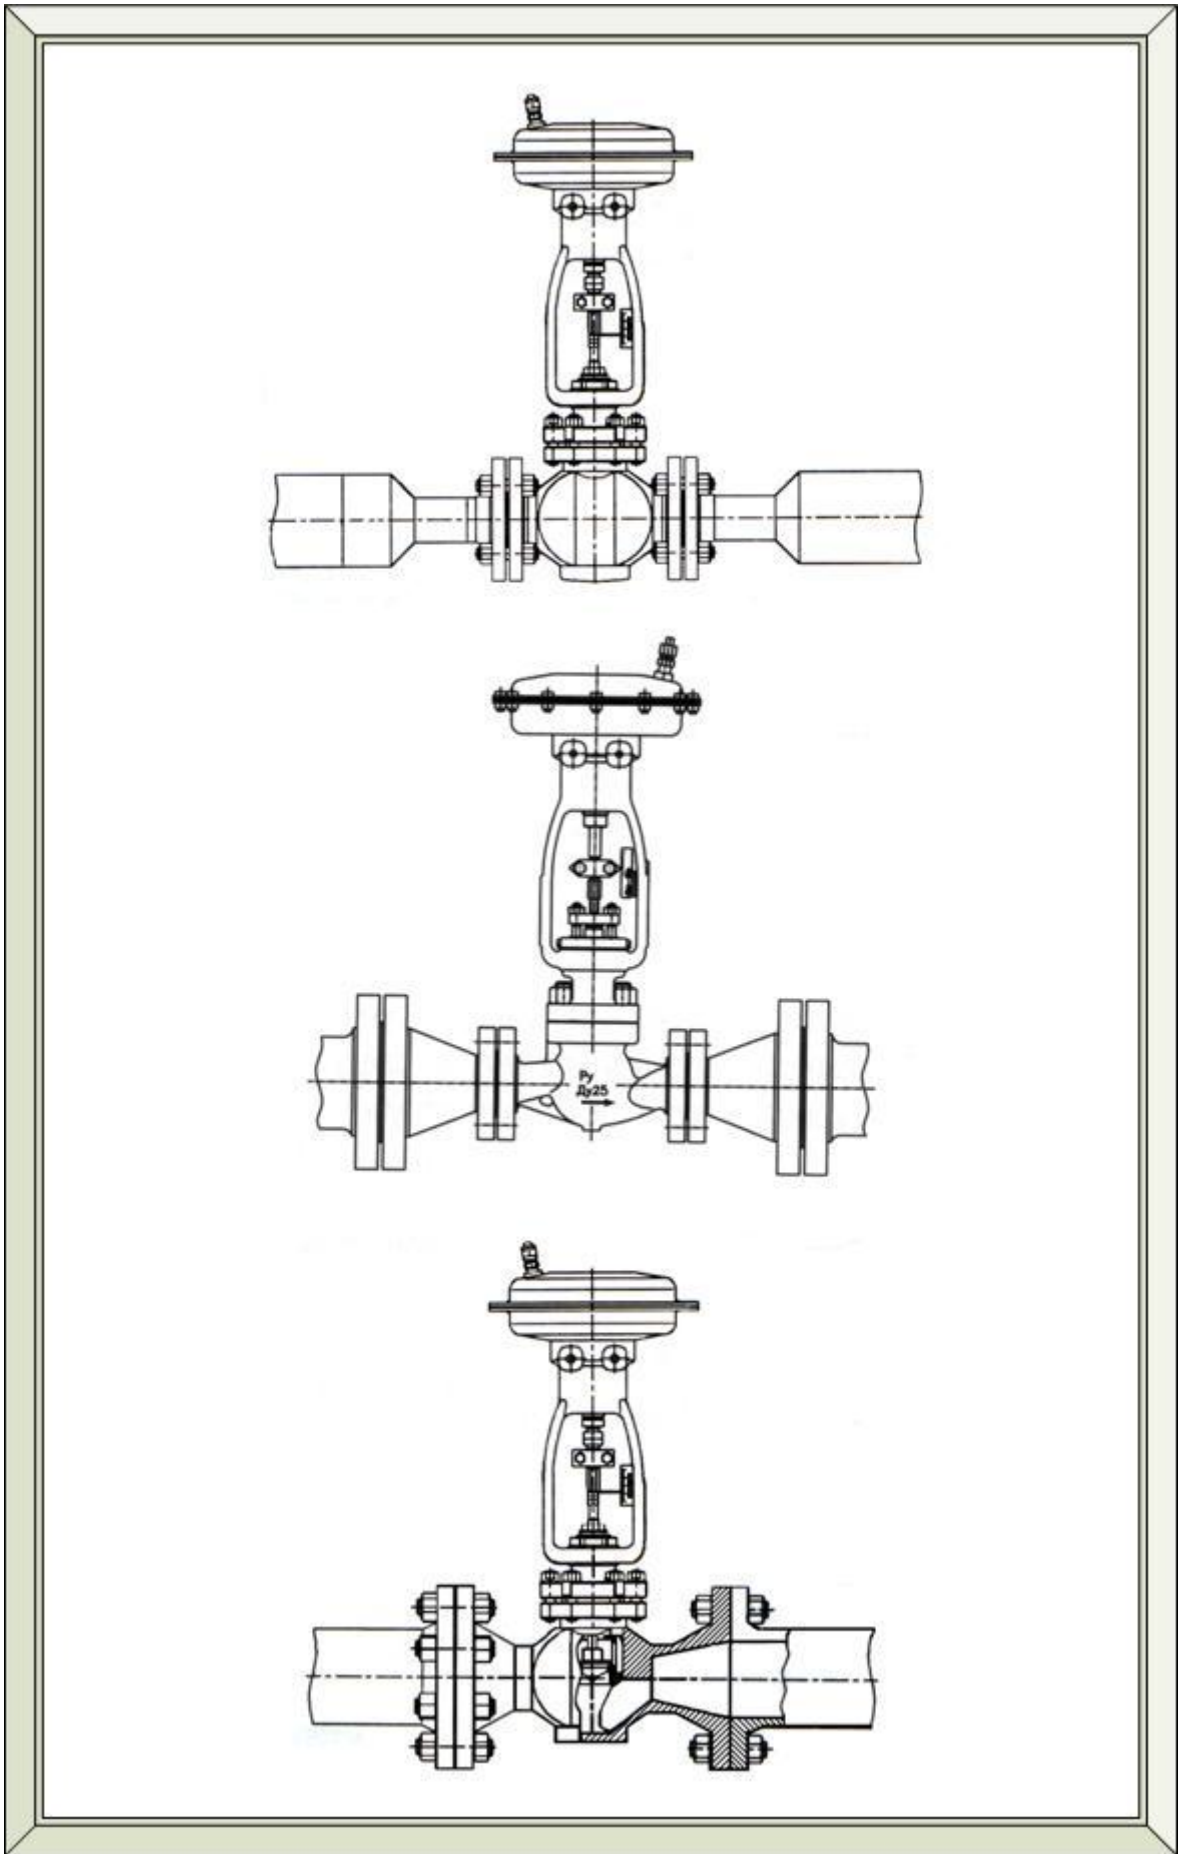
Монтажні схеми до закріплення регулювальних клапанів на трубопроводах.
